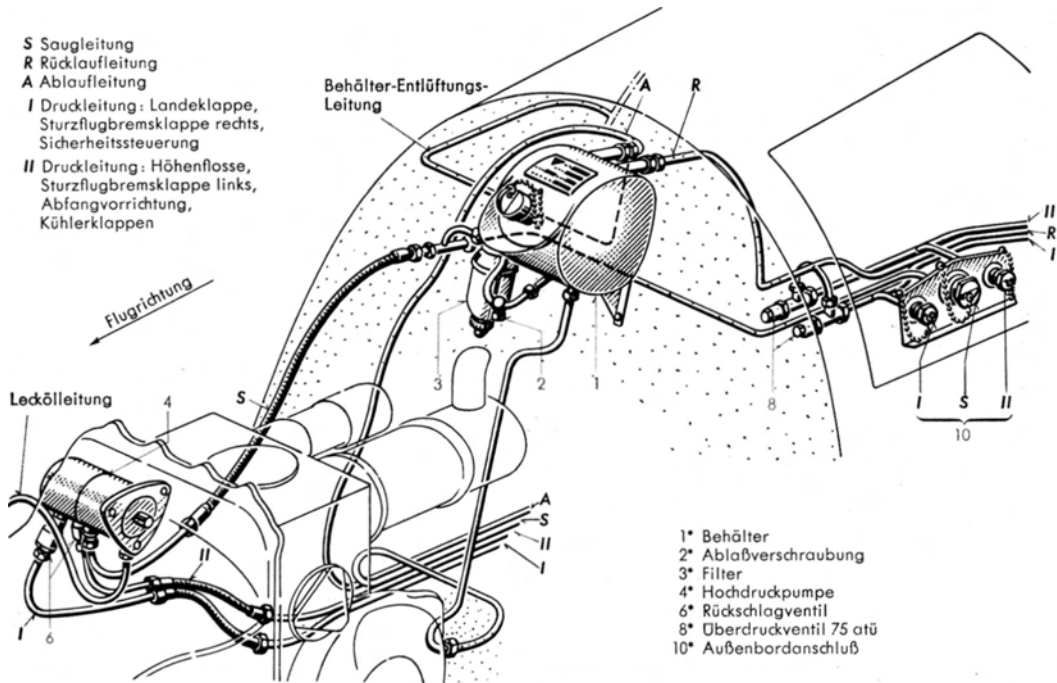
Übersicht der Drucköl-Anlage am Motor, Brandspant und Steuerungsbrücke
